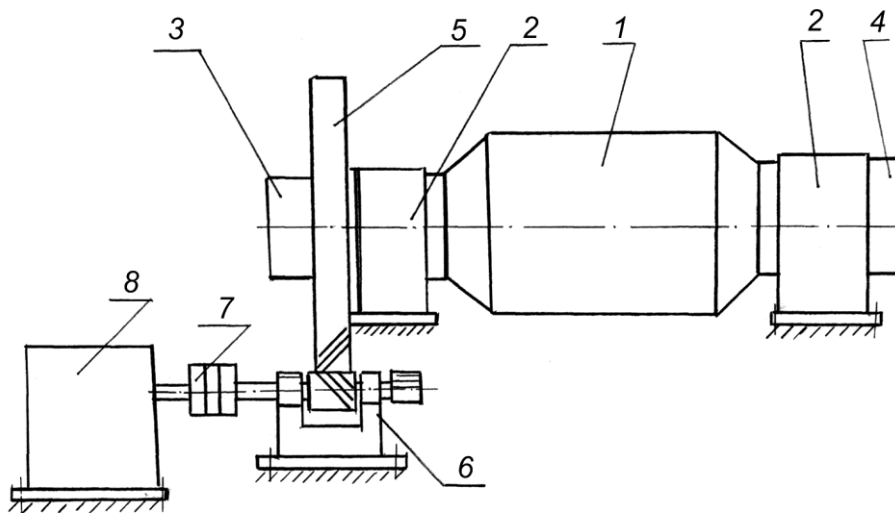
Кинематическая схема механической системы привода барабанной мельницы: 1 – барабан; 2 – подшипники; 3 – разгрузочная цапфа; 4 – загрузочная цапфа; 5 – зубчатое колесо; 6 – приводной узел; 7 – упругая муфта; 8 – синхронный электродвигатель
